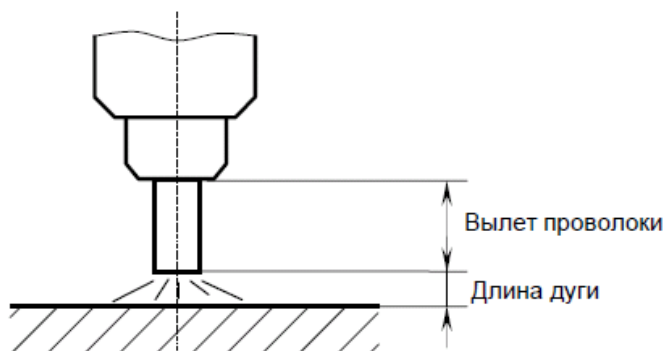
Вылет проволоки и длина дуги при сварке самозащитной порошковой проволокой
